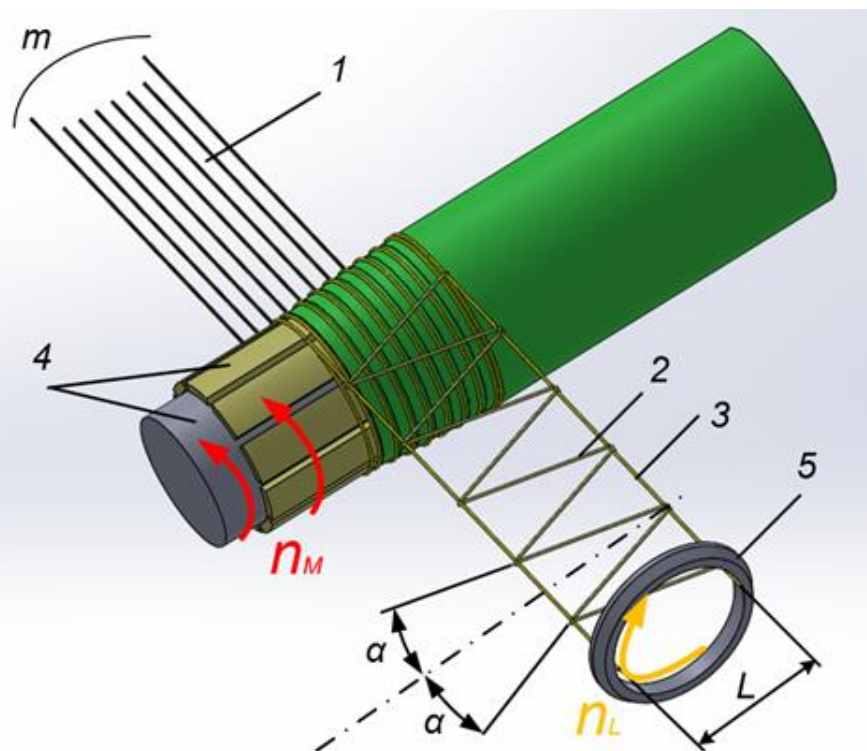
Схема укладання ниток: 1 – нитки поперечного армування;
